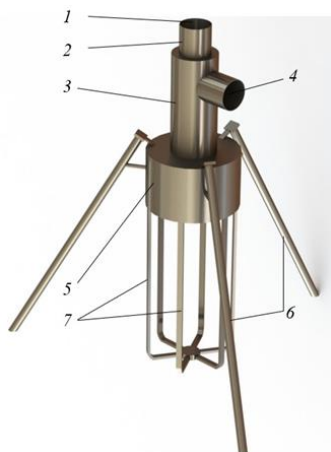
Трехмерная модель мультивихревого классификатора-сепаратора: 1 – входной патрубок; 2 – внутренняя цилиндрическая труба; 3 – внешняя цилиндрическая труба; 4 – выходной патрубок; 5 – цилиндрический блок; 6 – опоры; 7 – металлическая конструкция для съемной емкости
